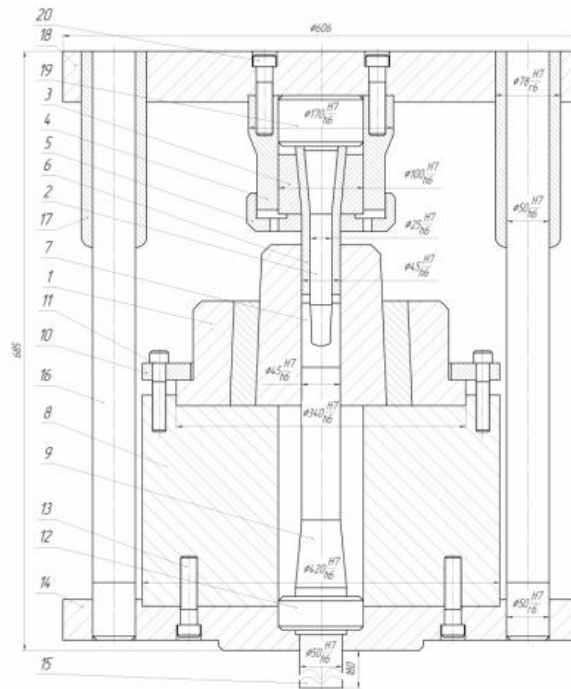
Креслення загального вигляду штампа для зворотного видавлювання
